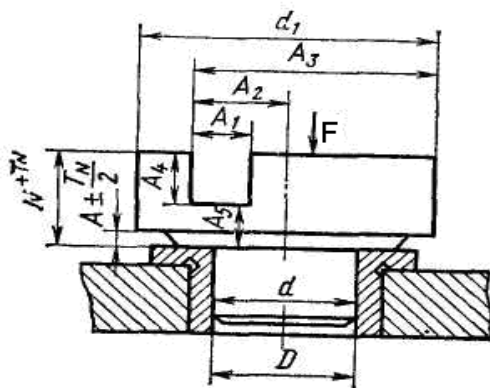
Схема установки заготовки при фрезеруванні пазу (до задачі 1.23.)
